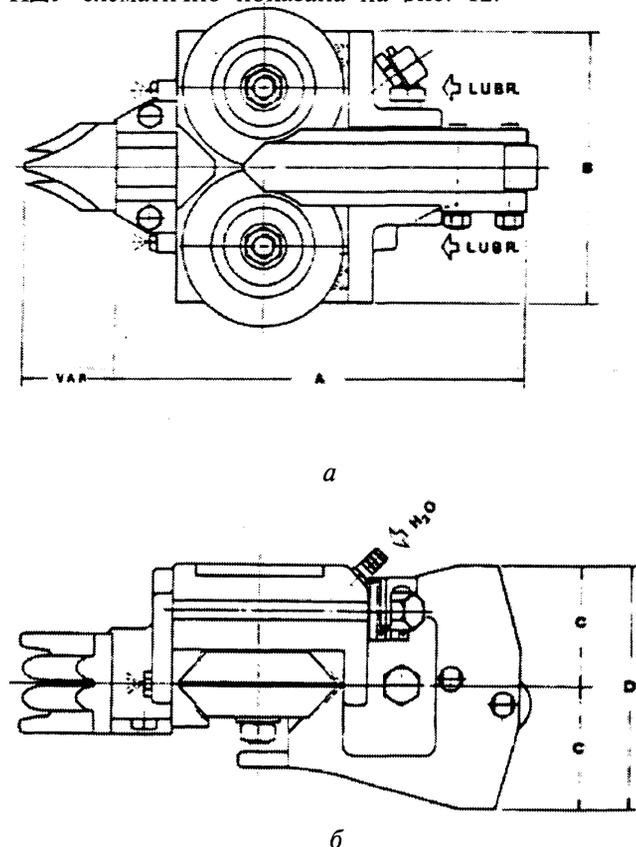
Конструкция делительного устройства с консольным расположением делительных роликов фирм MGS и «Daniely»: а – вид сбоку; б – вид сверху
